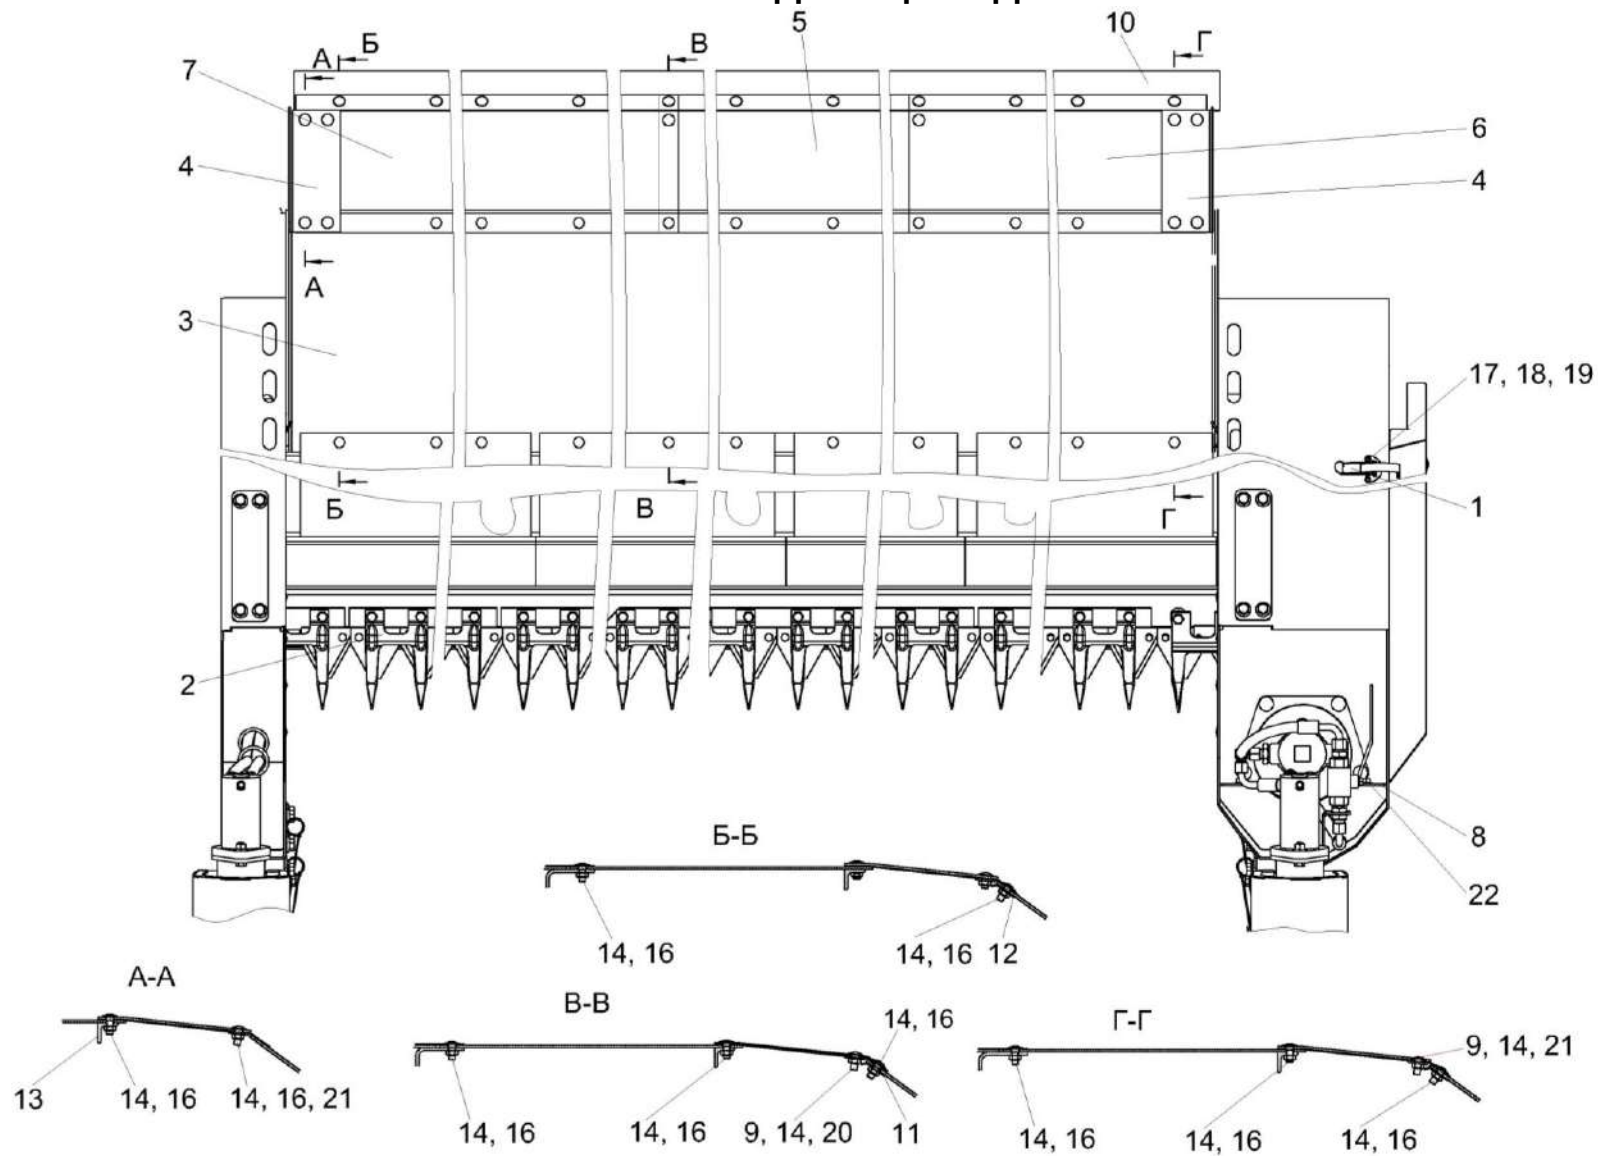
Приспособление для уборки рапса КЗК 2540000А (лист 1)
